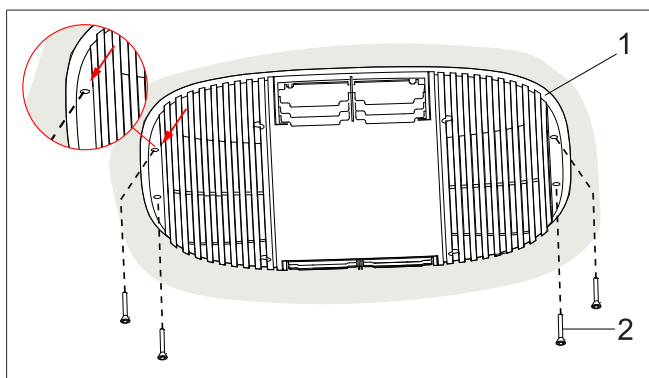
Befestigen des Luftverteilers am Fahrzeugdach
